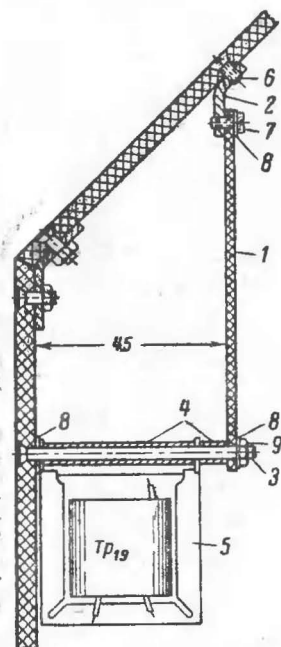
Крепление печатной платы кадровой развертки. 1 — печатная плата; 2 — уголки; 3 — стойка; 4 — втулки; 5 — импульсный трансформатор; 6 — винты М3 с потайной головкой; 7 — винты М3 с цилиндрической головкой; 8 — шайба; 9 — гайка М3.
